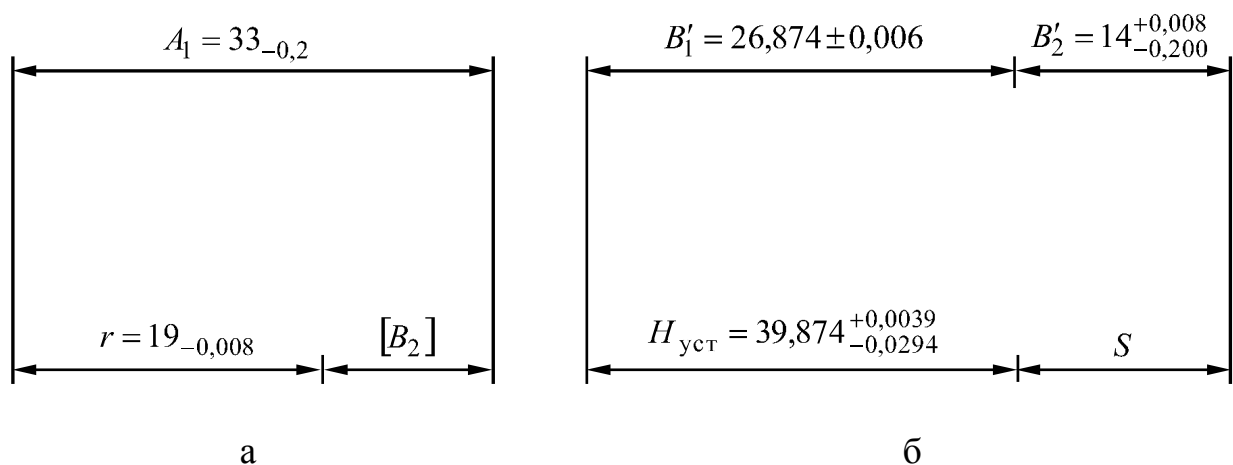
Схемы размерных цепей: а – поддетальная; б – сборочная
